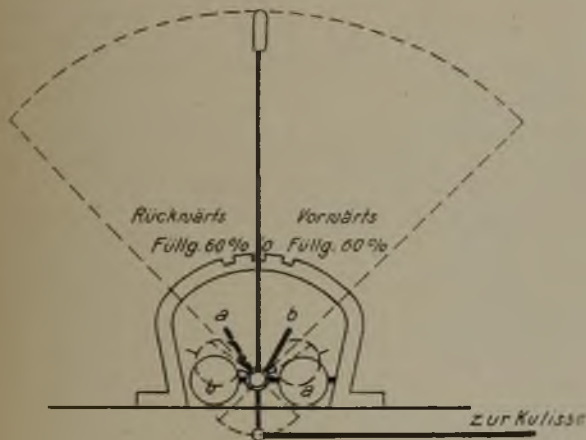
Schema eines Steuerbocks für einen Haspel mit Expansionsteuerung.
